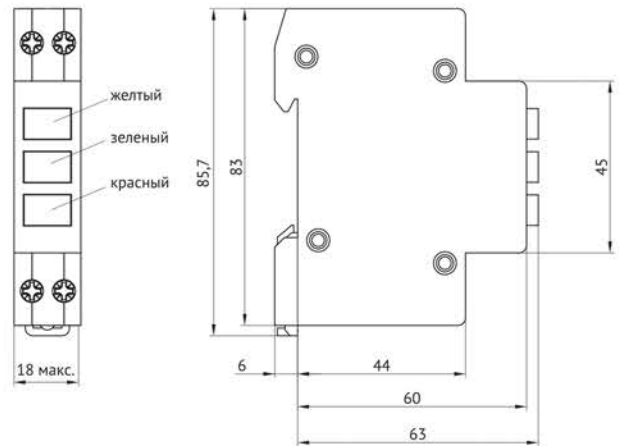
Габаритные, установочные и присоединительные размеры светового индикатора фаз типа OptiDin FSL63
